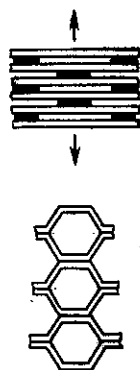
Изготовление сотового заполнителя растяжкой пакета фольги
